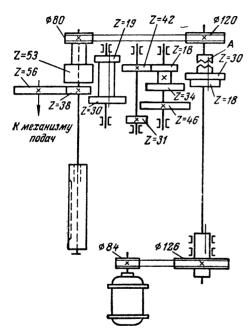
Кинематическая схема привода главного движения станка модели 2A420
